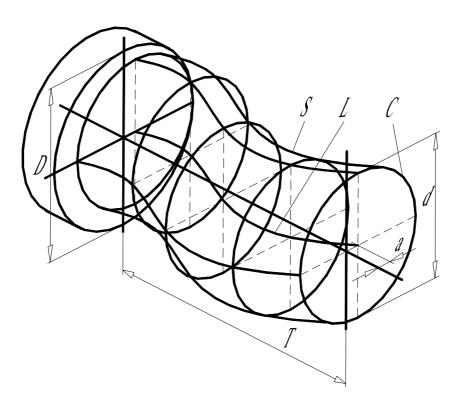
Геометрия рабочей поверхности ротора винтового насоса
